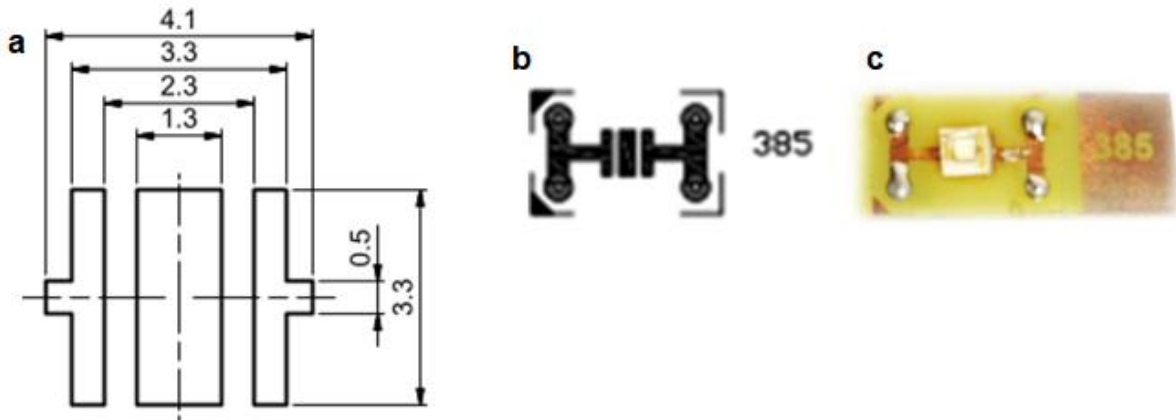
a). Medidas en mm para la soldadura, b).Diseño en AutoCAD y c). Montaje en una tarjeta PCB.
